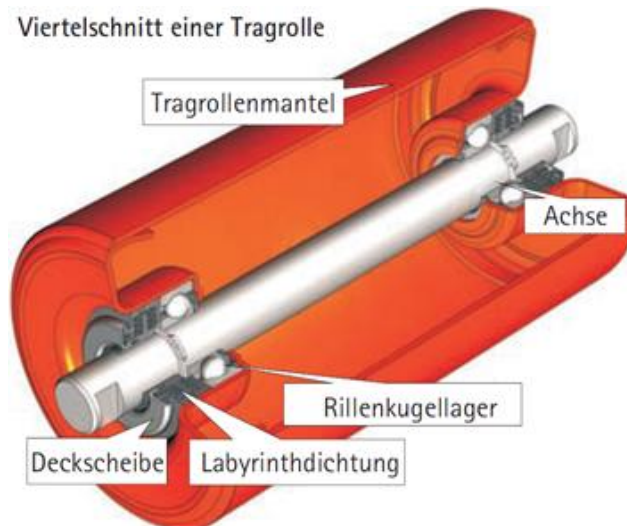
Schematischer Aufbau einer Tragrolle (Quelle: Sandvik Mining and Construction)
